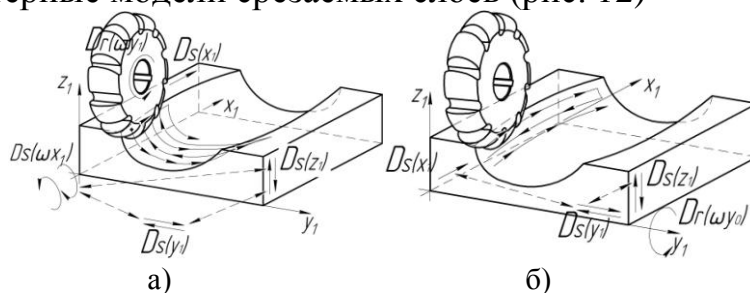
Схема обработки СФП: а – фрезерование с возвратно-качательным движением подачи дисковым инструментом; б – построчное фрезерование дисковым инструментом
